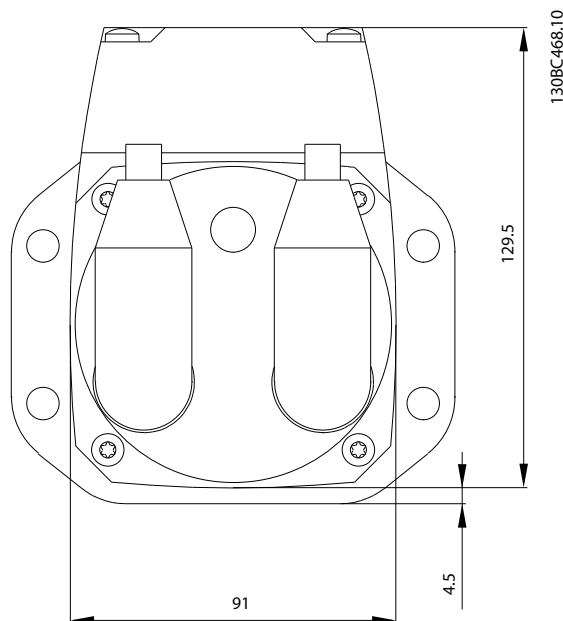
Rückansicht: Servomotor mit ISD Flansch, ohne Bremse
